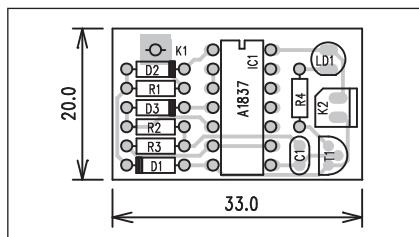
Obrazec desky spojů zesilovače (strana BOTTOM)
